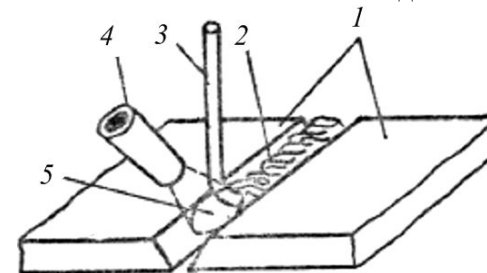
Газовая сварка с присадочным материалом:
